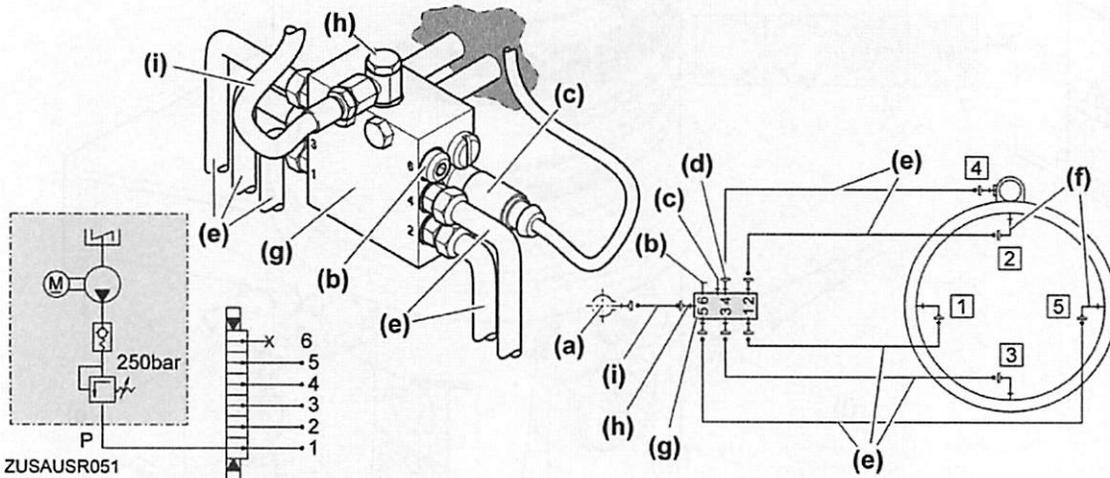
Verlegeplan und Hydraulik-Schaltplan (6er-Verteiler)
